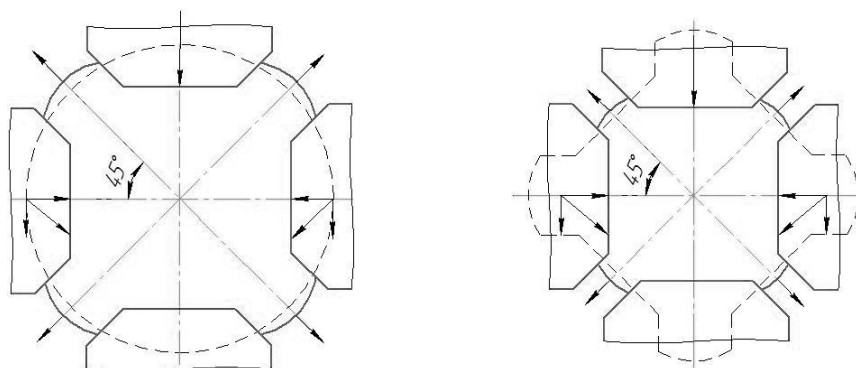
Схема обжатия заготовки круглого сечения с вытеснением металла между бойками
